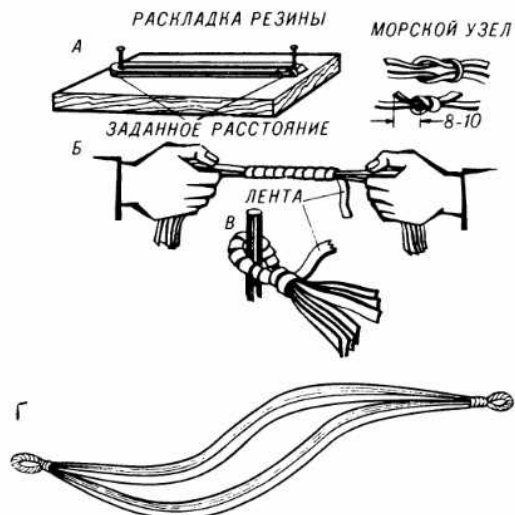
Изготовление резинового двигателя: А — укладка резины; Б, В — обматывание липкой лентой ушка; Г — готовый резиномотор.
